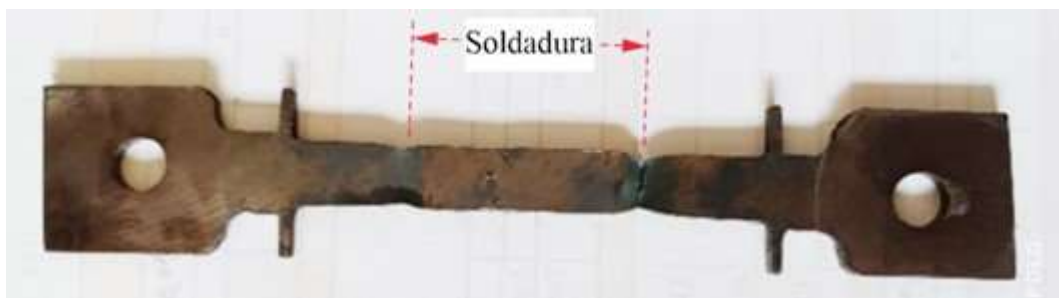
Tratamiento térmico post soldadura de 4 h a 730°C
